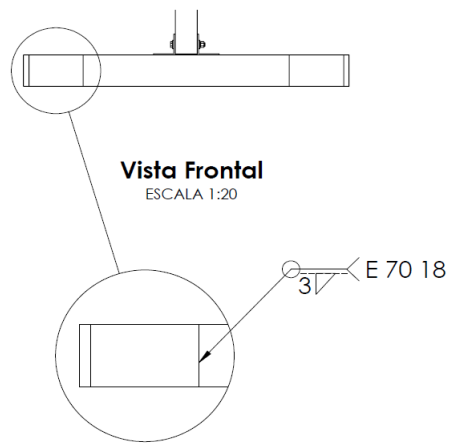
Soldadura a filete periférica por las placas de rigidizadores
